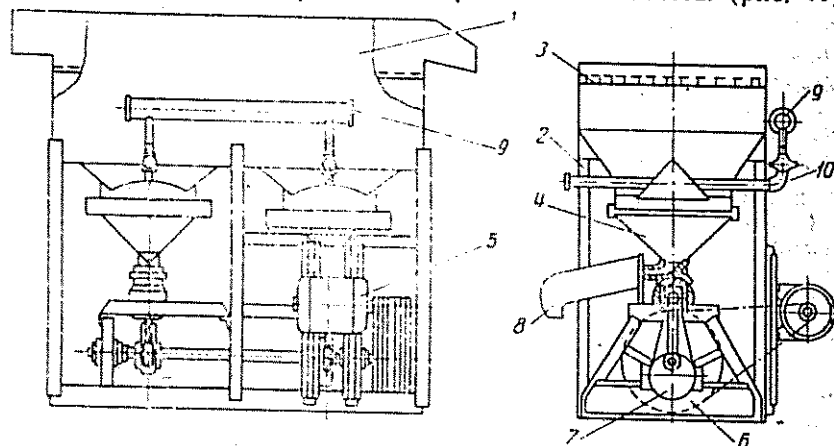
Отсадочная машина с подвижным конусом ПА-1, модель О-84: 1 — корпус машины; 2 — рама; 3 — решето; 4 — подвижный конус; 5 — электродвигатель; 6 — привод; 7 — эксцентрик; 8 — разгрузочное устройство; 9 — труба для подпрессетной воды; 10 — патрубок для подачи подпрессетной воды
